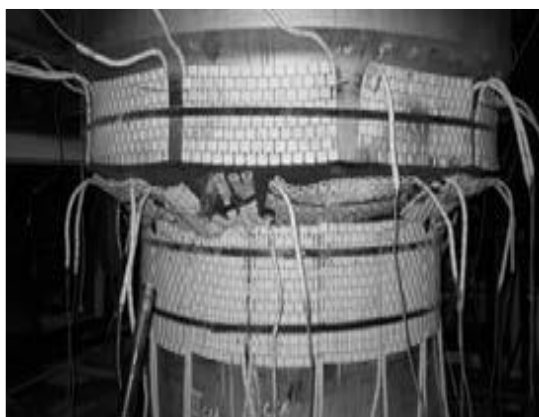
Расположение нагревателей на приспособление для нагрева внутренней стороны сварного соединения.
